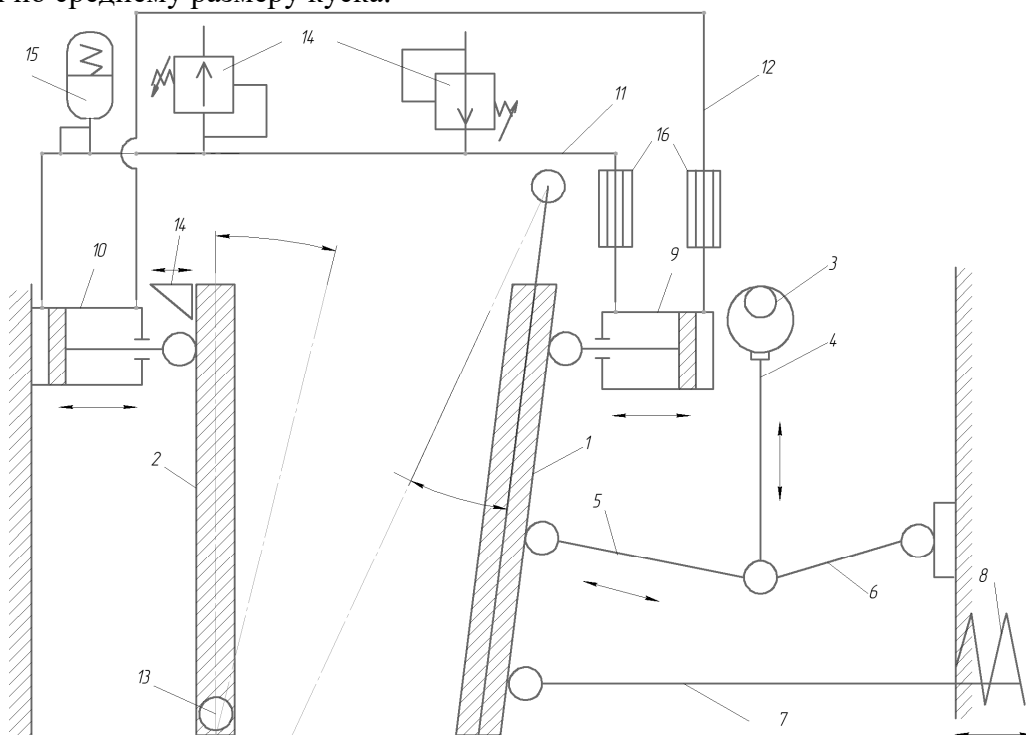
Предлагаемая конструкция щековой дробилки с двумя подвижными щеками с гидравлическим приводом
